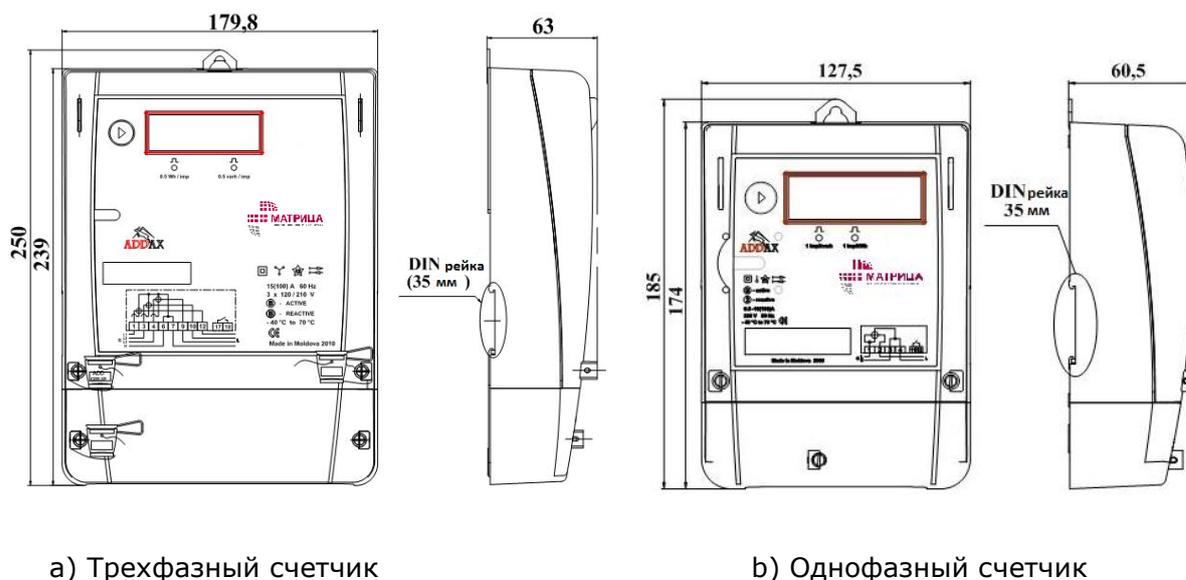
Общий вид и габаритные размеры счетчика с укороченной крышкой клеммника
